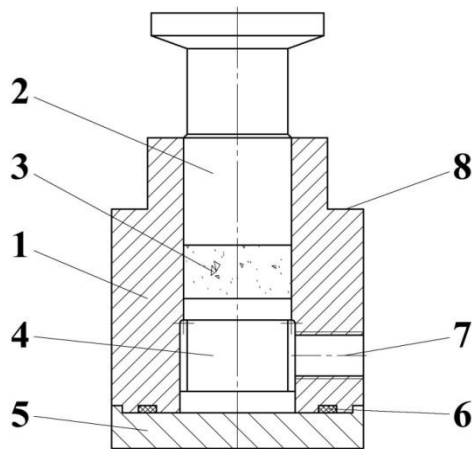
Пресс-форма: 1 – матрица; 2 – верхний пуансон; 3 – порошок; 4 – нижний пуансон; 5 – крышка; 6 – прокладка; 7 – отверстие для подвода / отвода воздуха; 8 – заплечики для фиксации матрицы на столе копра
